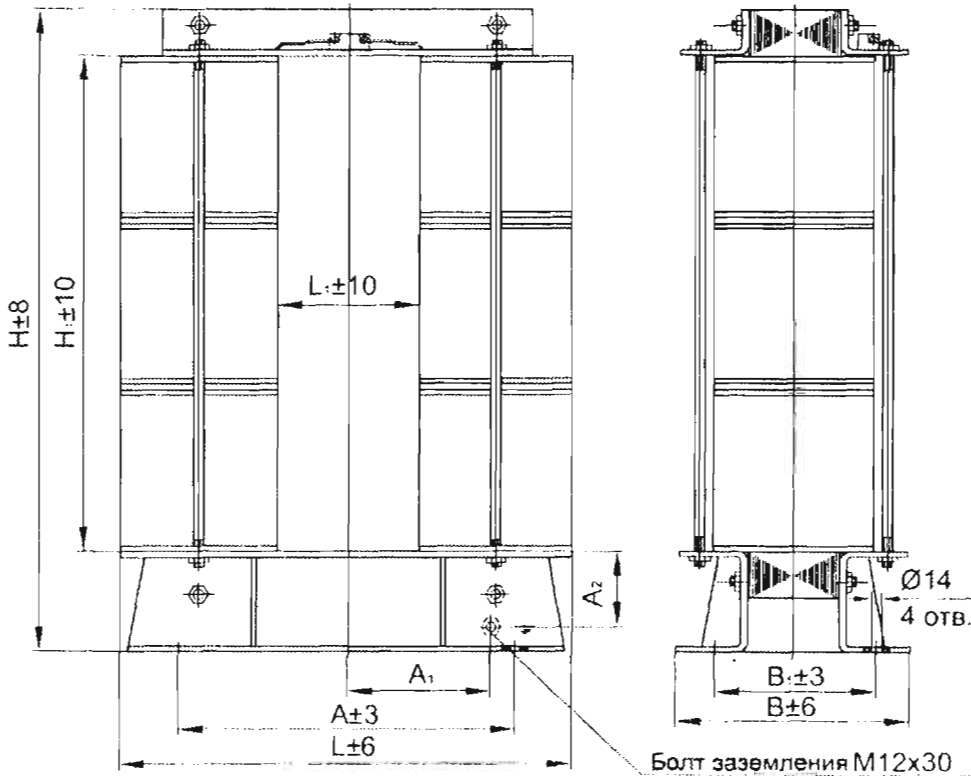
Общий вид, габаритные и установочные размеры трансформаторов тока ТНШ-0,66
